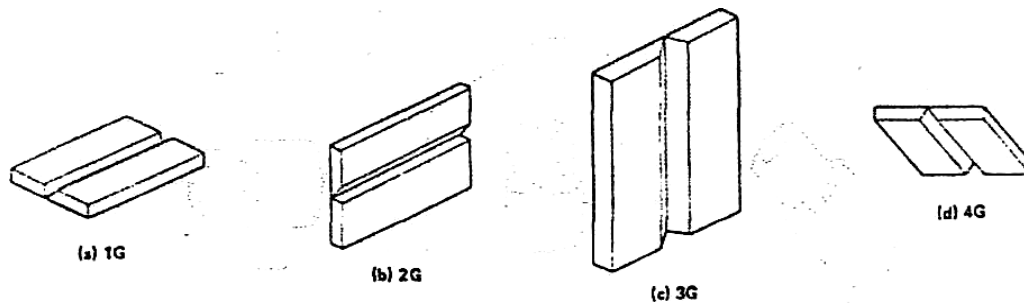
Posiciones de Soldadura en placas con soldadura de ranura.
